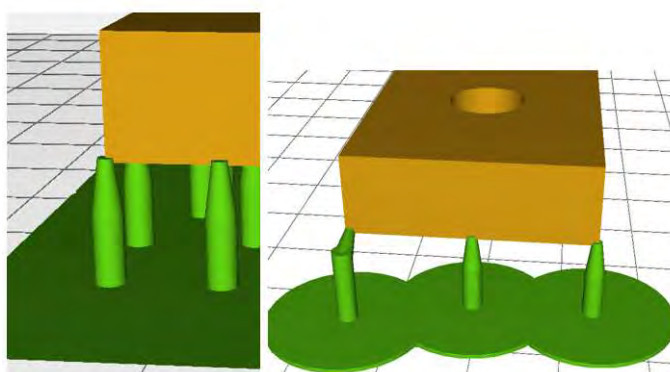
Structura geometrică a elementelor constructive pentru sonda generată
